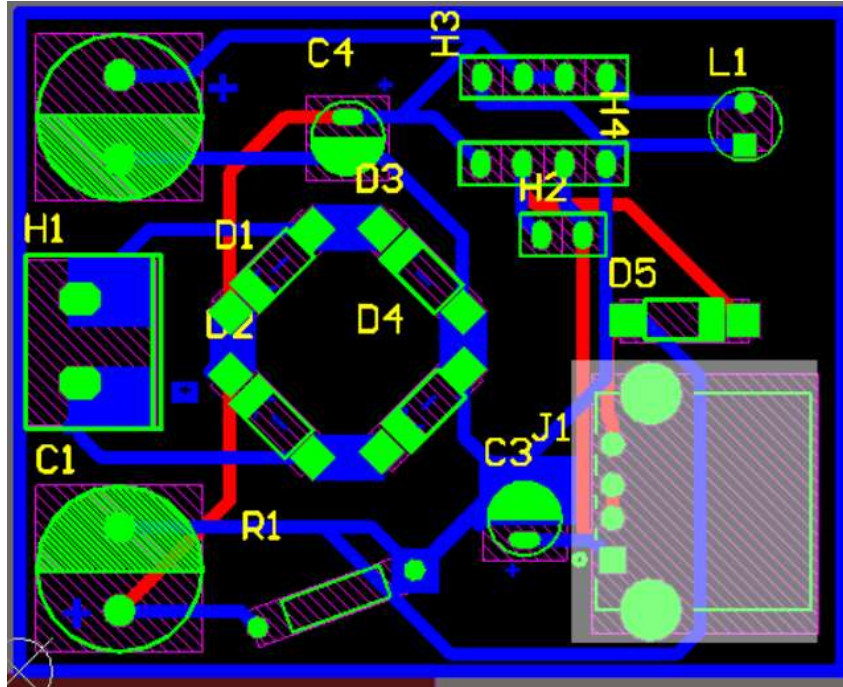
Diseño de las pistas para su implementación en placa fenólica en Altium Designer. Fuente propia.
